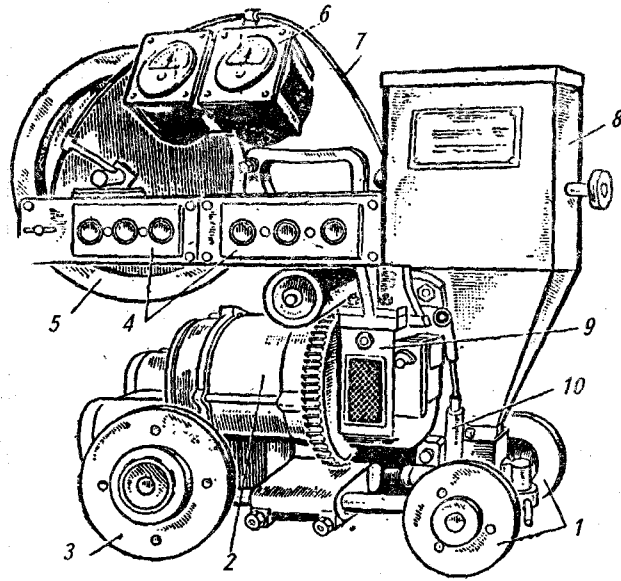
Сварочный трактор ТС-17М: 1 — направляющие колеса; 2 — электродвигатель для подачи электродной проволоки и передвижения трактора; 3 — ведущие колеса; 4 — пульт с кнопками управления; 5 — кассета с электродной проволокой; 6 — электроизмерительные приборы; 7 — электродная проволока; 8 — бункер для флюса; 9 — механизм подачи проволоки; 10 — мундштук
